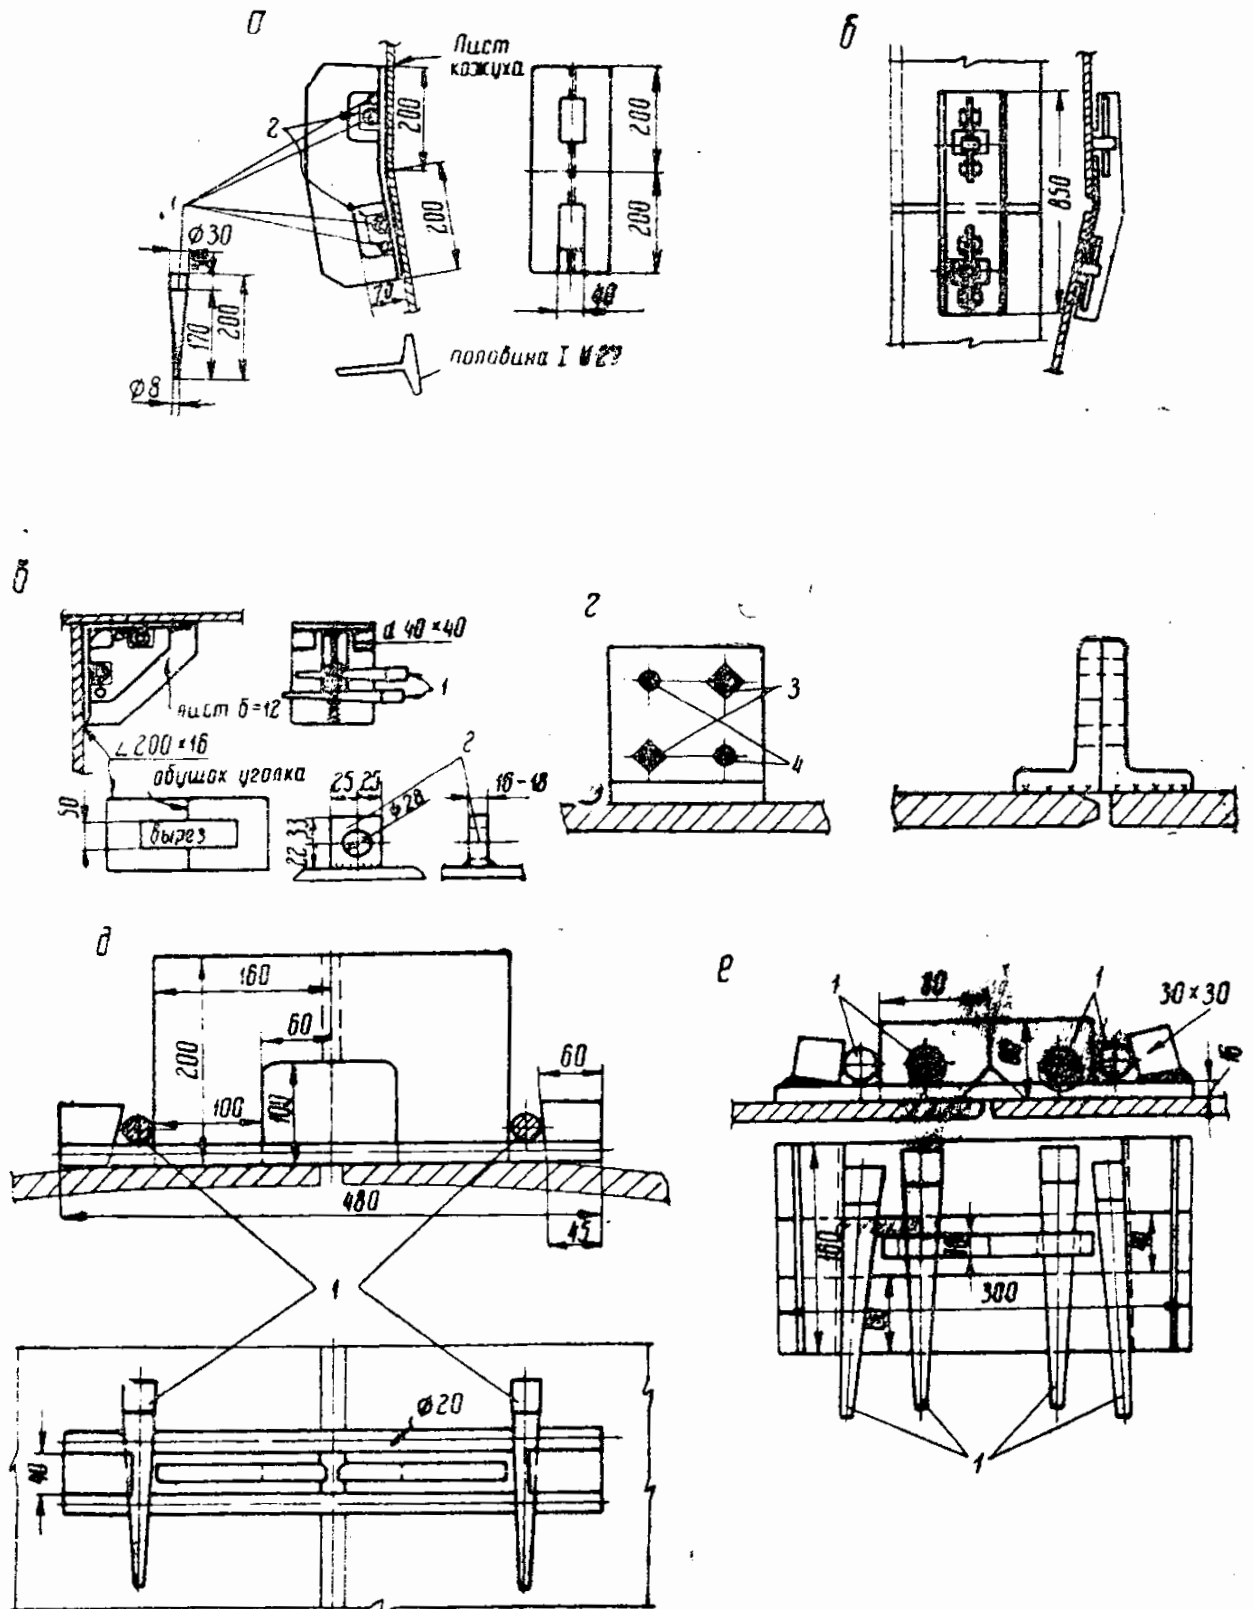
Инвентарные приспособления для сборки листовых конструкций: а — стяжной тавр на перегибе; б — стяжной швеллер на перегибе; в — стяжной угольник; г — фиксаторы — парные уголки; д — фиксаторы-скобы; е — фиксаторы-шайбы; 1 — клинья; 2 — шайбы; 3 — болт; 4 — пробка.
